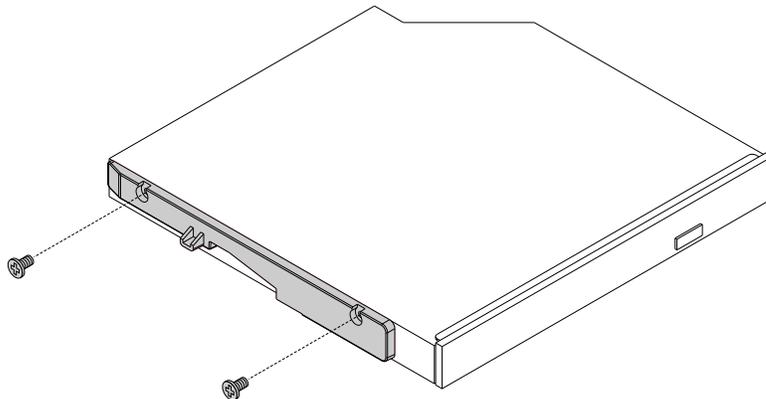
Halterung für flaches optisches Laufwerk installieren
